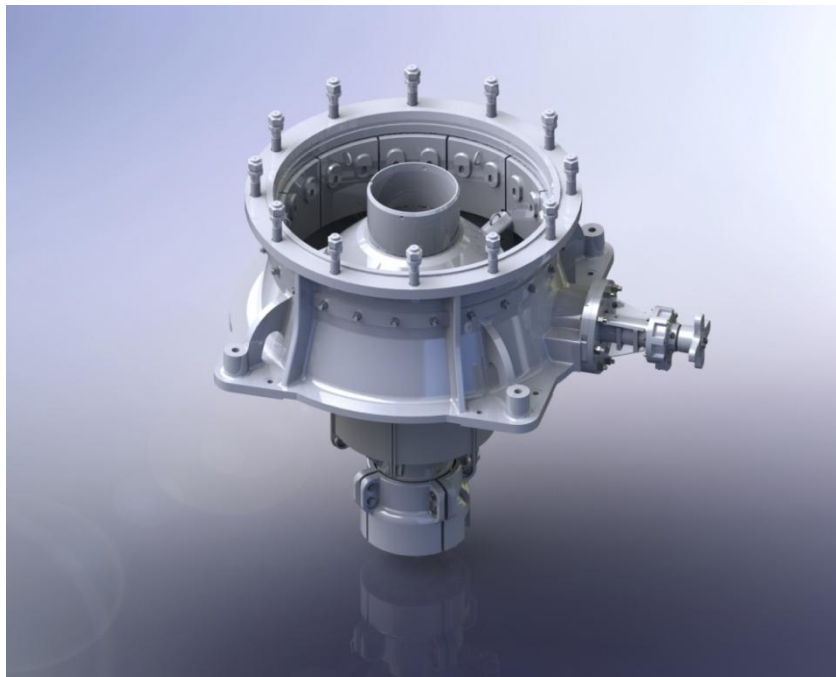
Комп'ютерна модель дробарки конусної КРД 700-75
